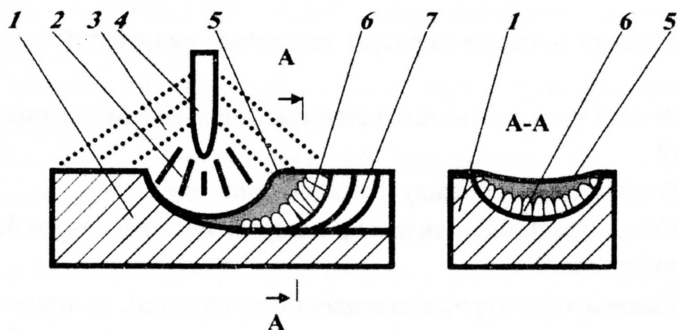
Схема дуговой сварки в среде защитных газов:
